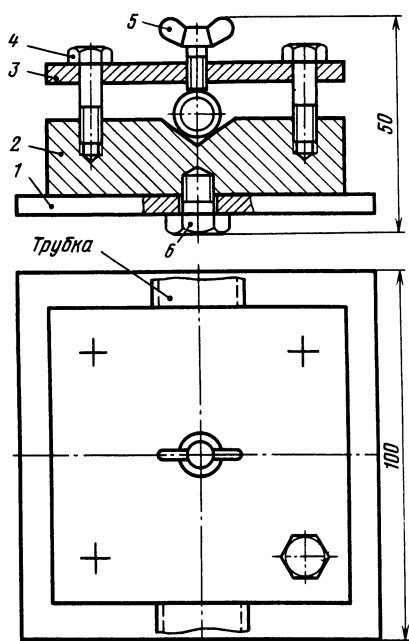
Чертеж приспособления для сверления отверстий в трубках.
